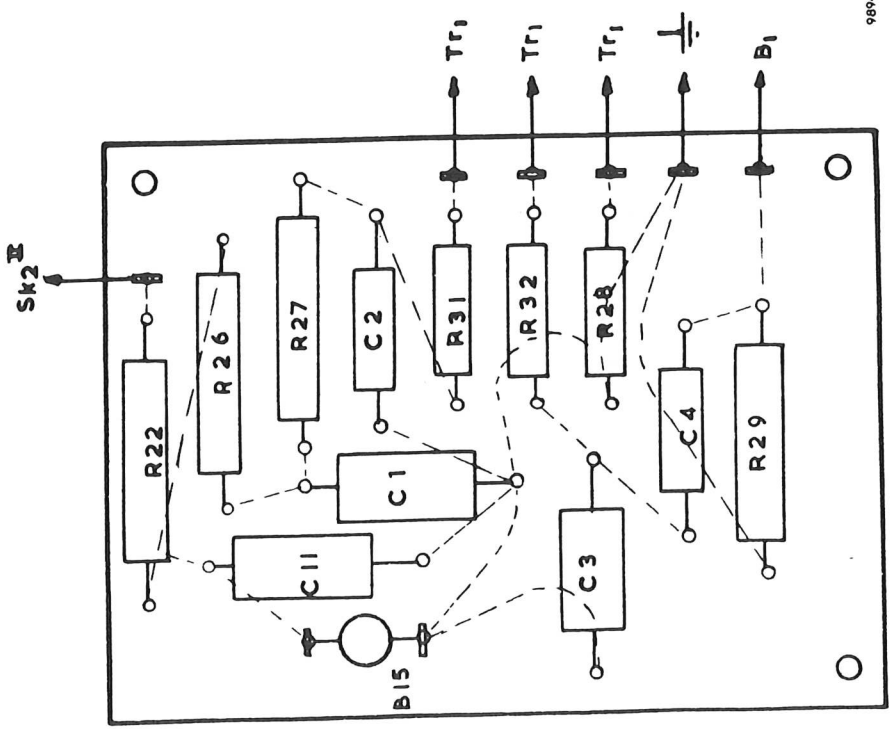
Plan de branchement de la plaque de câblage imprimé B (voir fig. 9)
